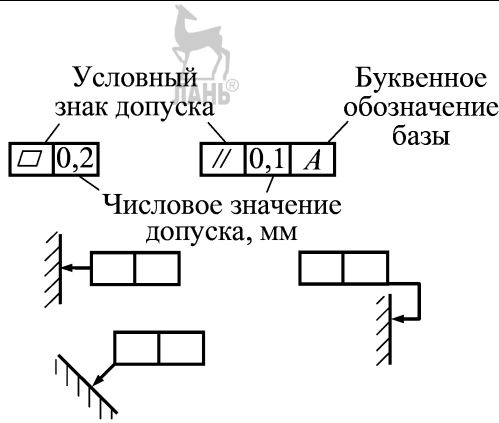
Условные обозначения допуска формы и расположения поверхностей
